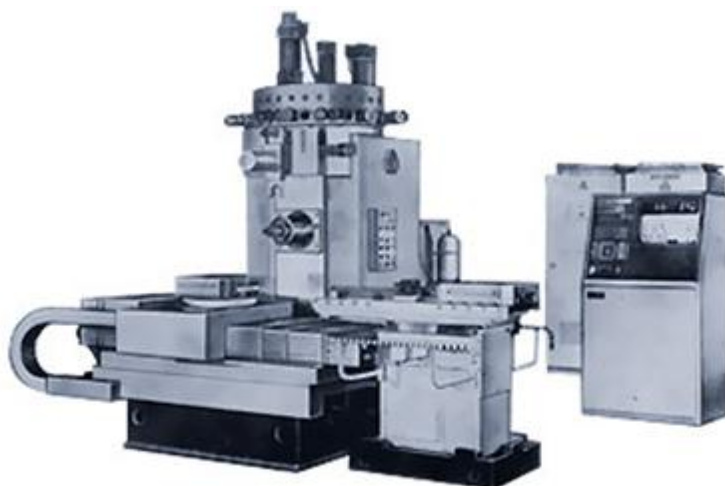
Общий вид обрабатывающего центра IP500ПМФ4.
